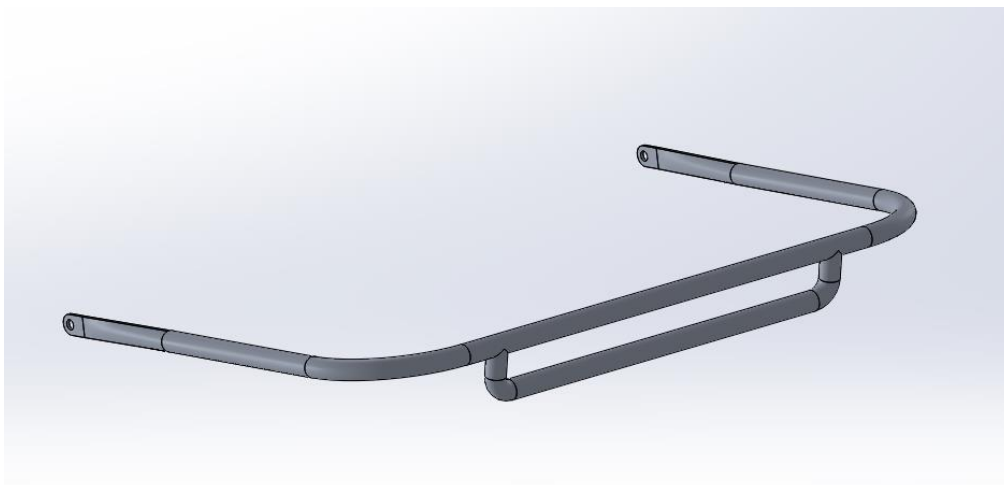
parte superior paragolpes frontal. Fuente: propia.
